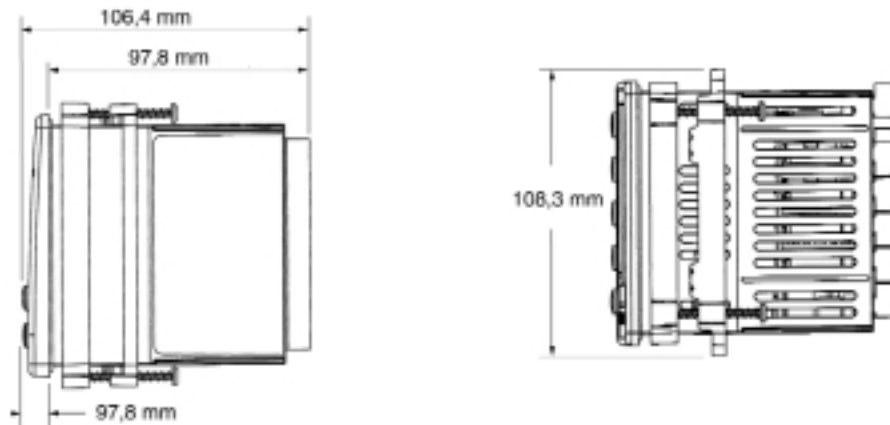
Vue latérale, vue de dessus et dimensions.
